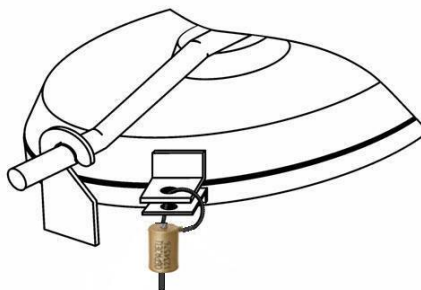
Схема установки ЗПУ на штурвале разгрузочного люка вагона-хоппера для цемента
